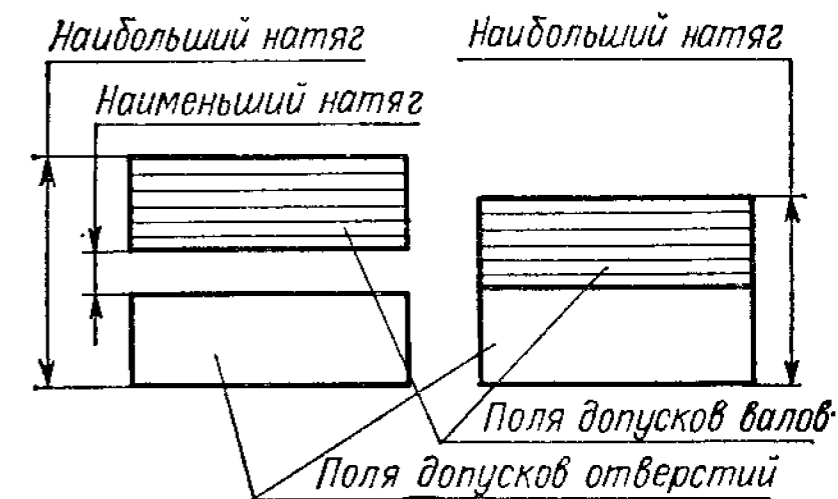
Посадка с натягом (поле допусков отверстия расположено под полем допуска вала)
